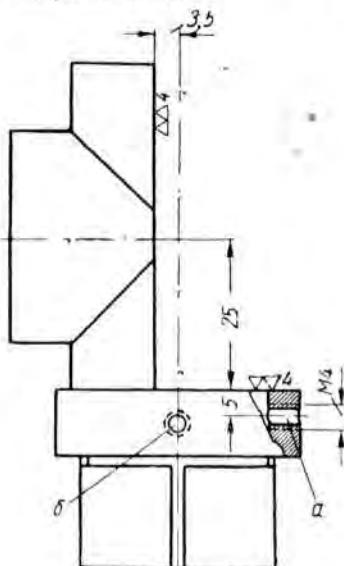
Корпус фонарика К-101 и КПС, распиленный для установки патрона ПЧЛ
